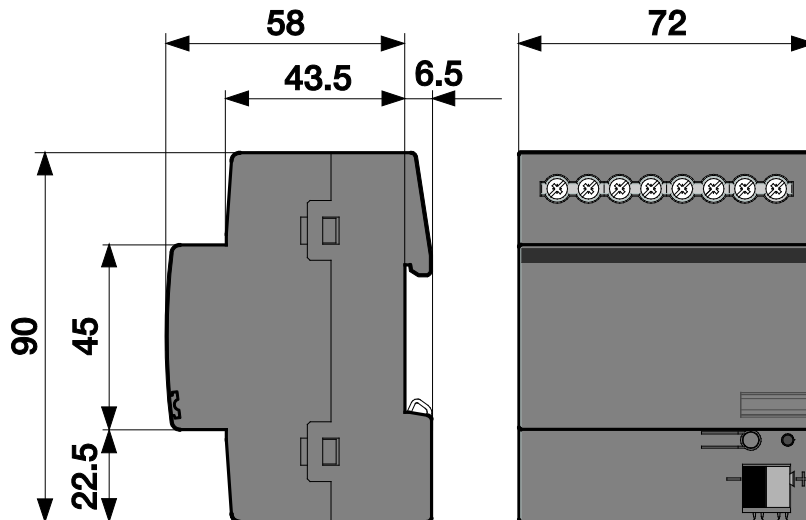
Dimensions de l'actionneur de chauffage sextuple
